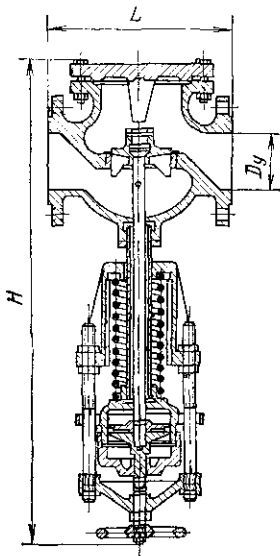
Клапан редукционный пружинный фланцевый 18ч26р
